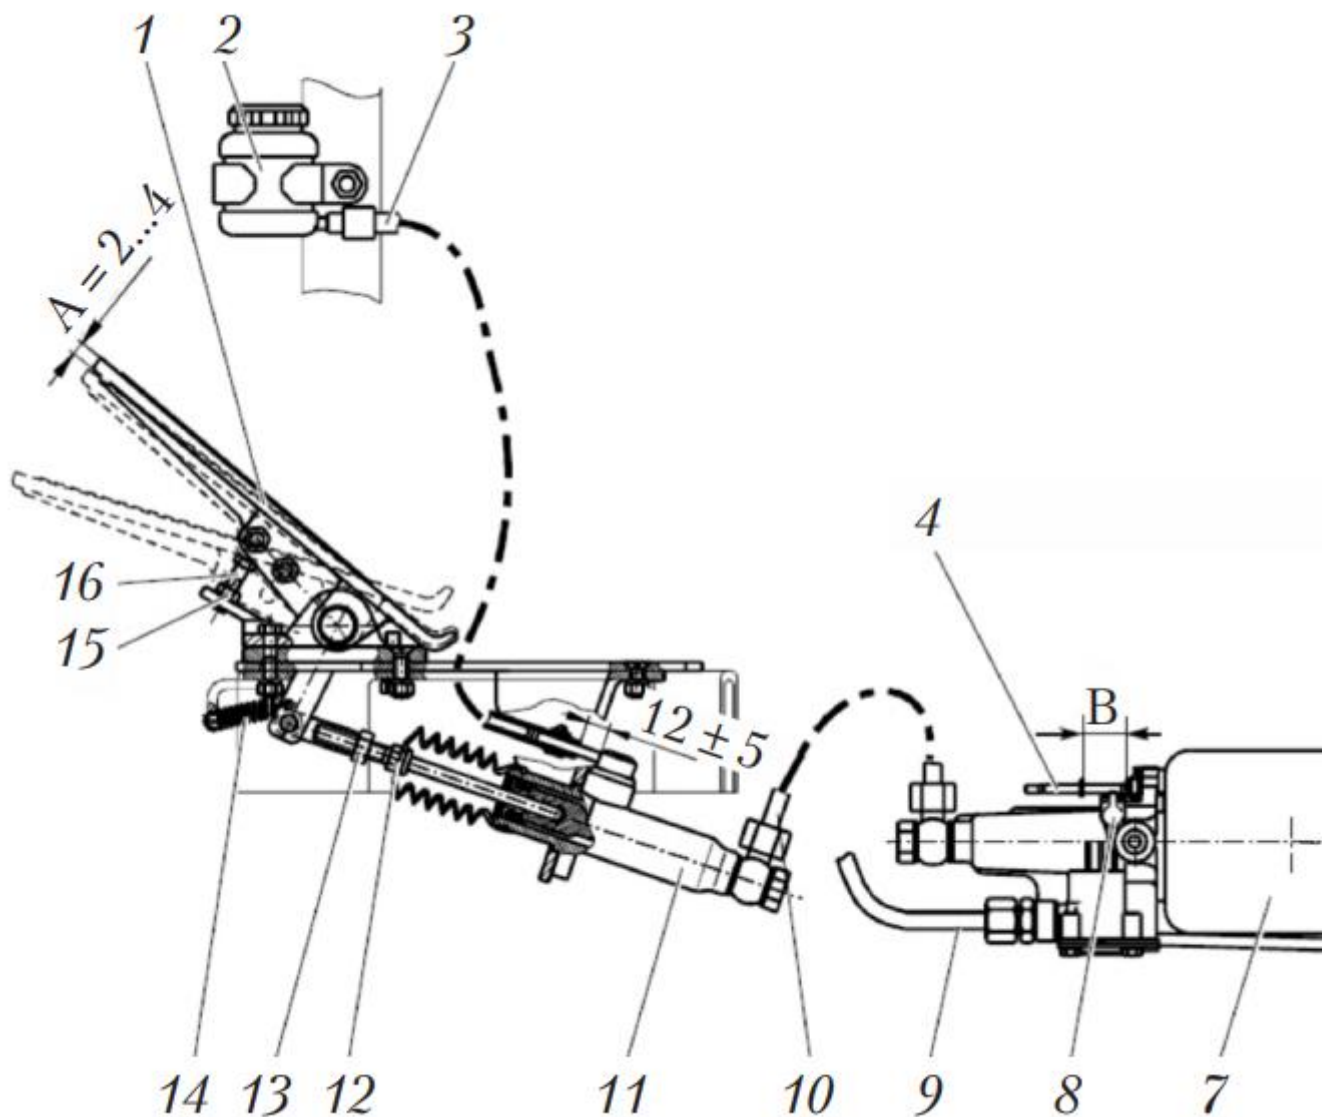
Схема гидропневматического привода сцепления: А — свободный ход на конце педали сцепления; В — ход толкателя; В — величина выхода индикатора износа ведомого диска; 1 — педаль; 2 — резервуар для тормозной жидкости; 3, 10 — гидравлические трубопроводы; 4 — датчик износа ведомого диска; 5, 12 — толкатели; 6 — рычаг-вилка; 7 — пневмогидроусилитель; 8 — клапан прокачки; 9 — воздушный трубопровод; 11 — подпедальный цилиндр; 13, 15 — контргайки; 14 — оттяжная пружина; 16 — упор
